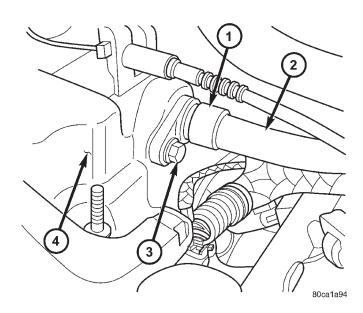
LOCALIZACION DE LA VALVULA DE PCV - MOTOR 2.4L
